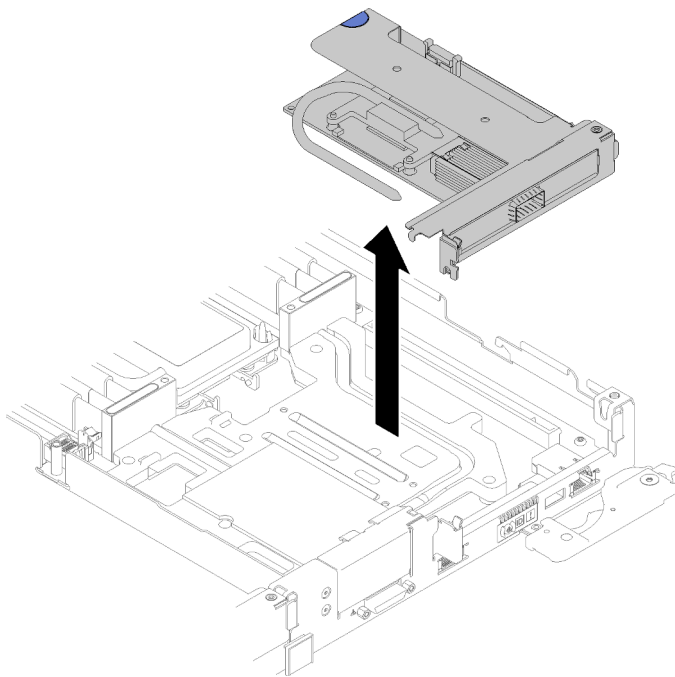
Entfernen der Gehäusebaugruppe für PCIe-Adapterkarte
